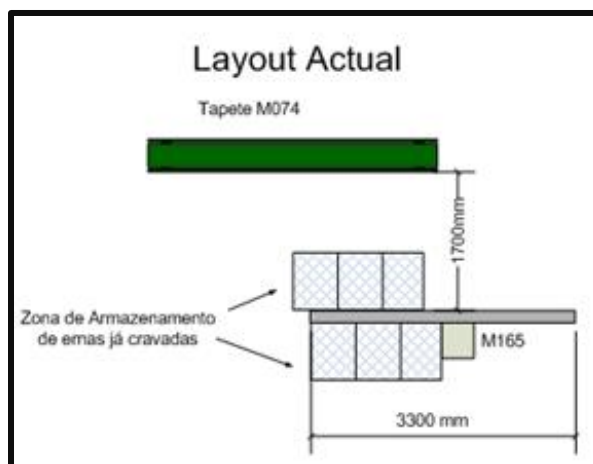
LAYOUT ATUAL DA MÁQUINA EM ESTUDO
